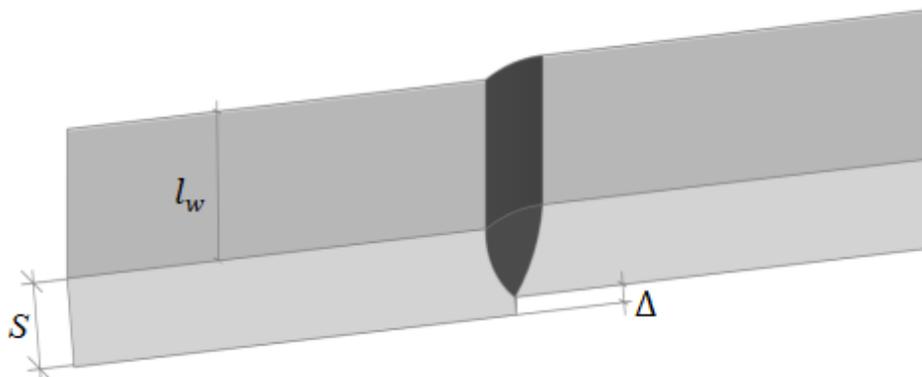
Сварной стыковой шов со смещением кромок свариваемых элементов
